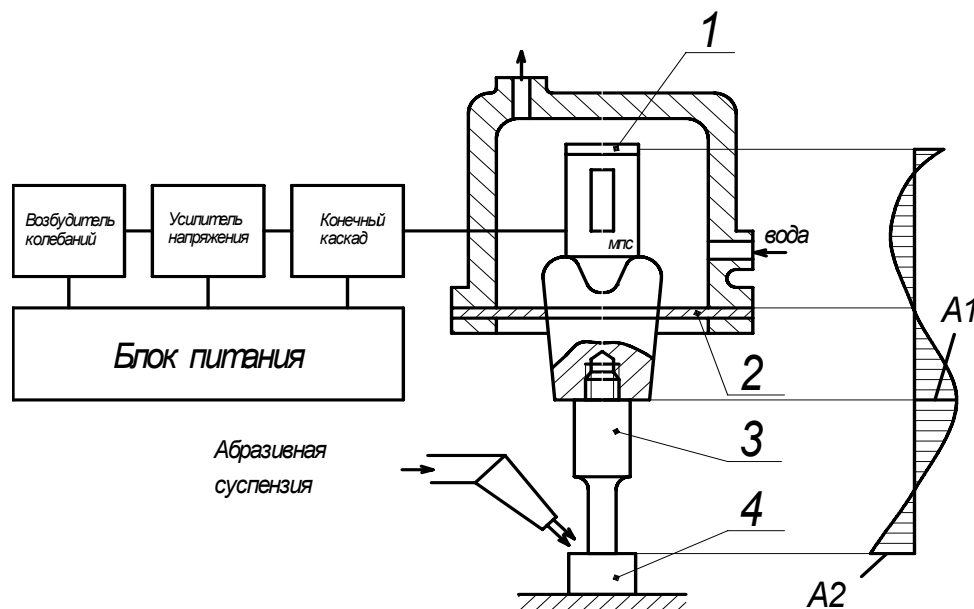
Принципиальная схема генератора: 1 – резиновая накладка; 2 – опорный фланец; 3 – концентратор (двухполуволновый); 4 – обрабатываемая заготовка; МПС – магнито-стрикционный преобразователь
